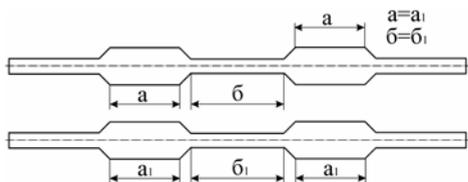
Проверка бокового зазора прокатыванием проволоочки или пластинки из свинца
